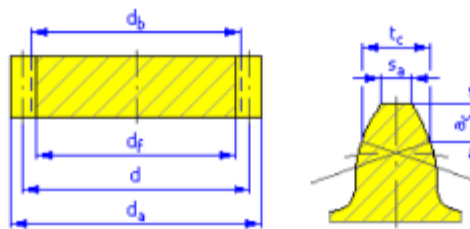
Resultados geométricos de los engranajes cónicos. Fuente: Inventor, 2019.
